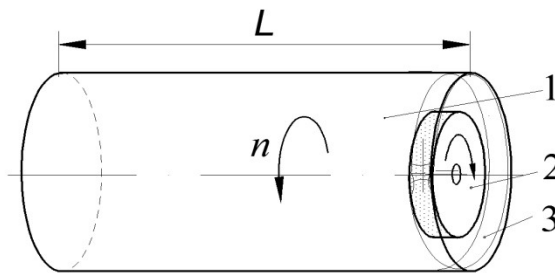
Схема обработки внутренней поверхности цилиндра:
